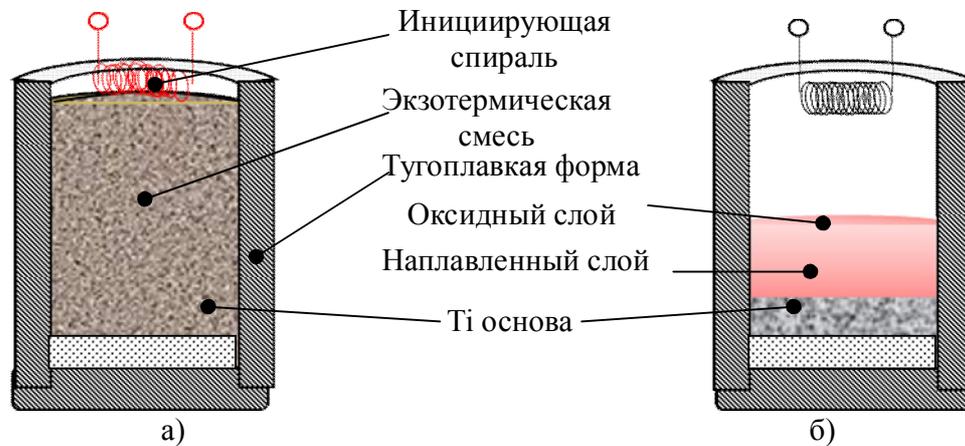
Схема нанесения СВС-наплавки: а) образец перед синтезом, (б) образец после синтеза.
